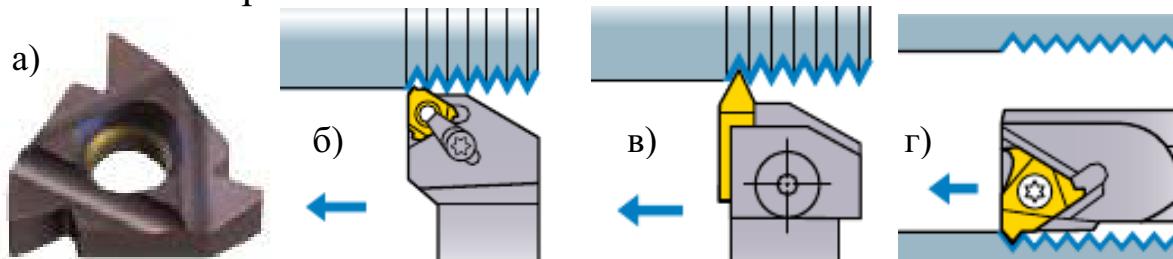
Инструмент для нарезания резьбы: а – изображение сменной пластины; б, в – резцы для нарезания внешней резьбы; г - резцы для нарезания внутренней резьбы
